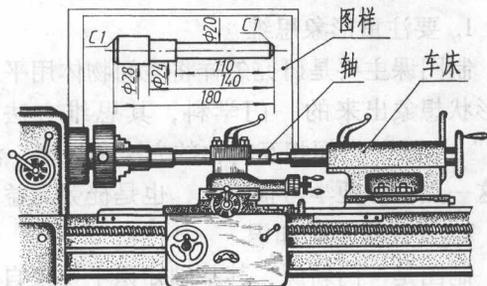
装配体、装配图, 零件、零件图及依据图样加工零件
